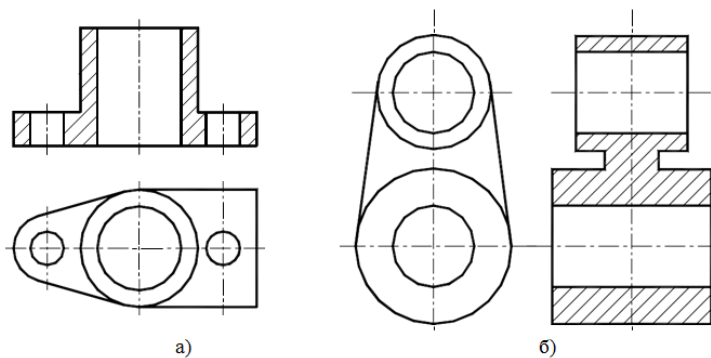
а) разрез фронтальный; б) разрез профильный
